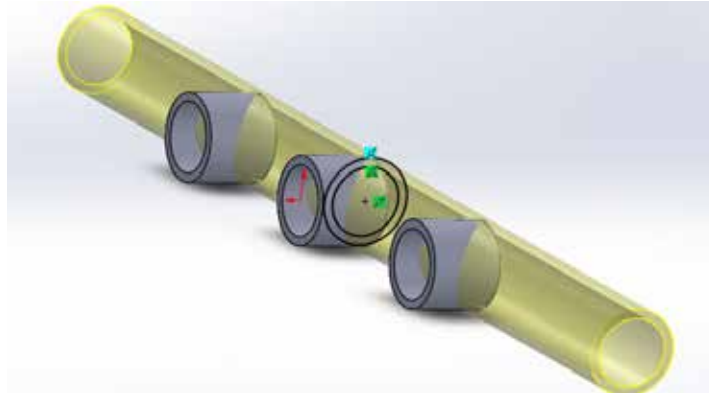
Croquis y extrusión 2, del Manifold de Alta.
